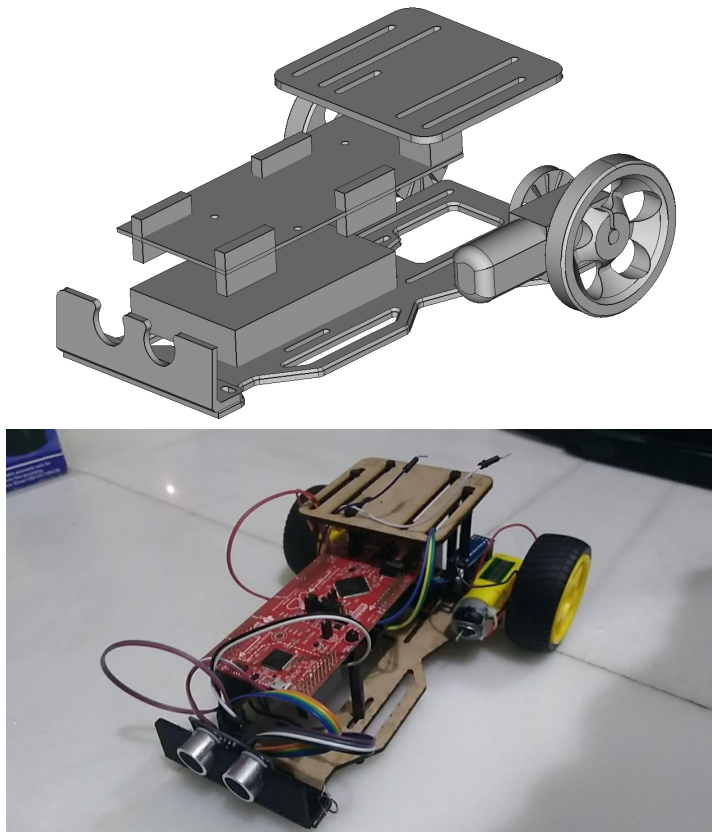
Diseño en FreeCAD frente a diseño ensamblado.
